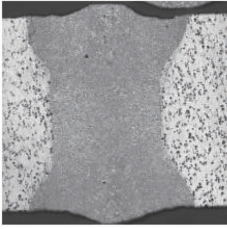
光纤激光焊接接头典型形貌(4.5 kW,60 J/mm)
